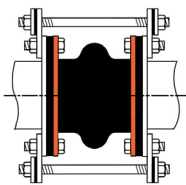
Приклад зумового з'єднання з анкерними шпильками
